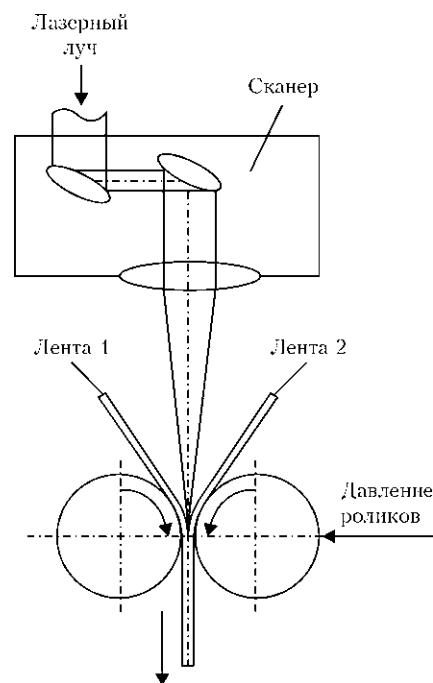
Схема гибридной лазерно-прессовой сварки
